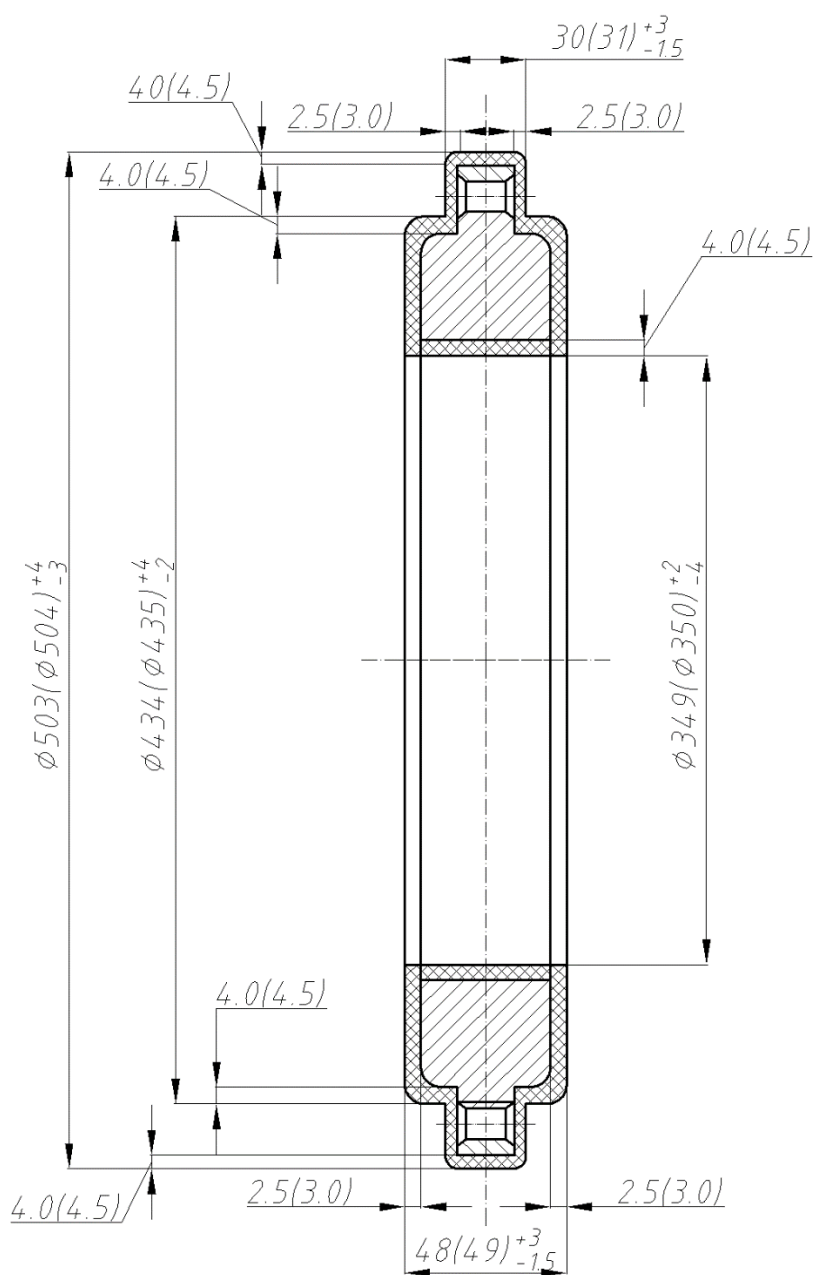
Креслення заготовки деталі «Шестерня МБК34М4568»
